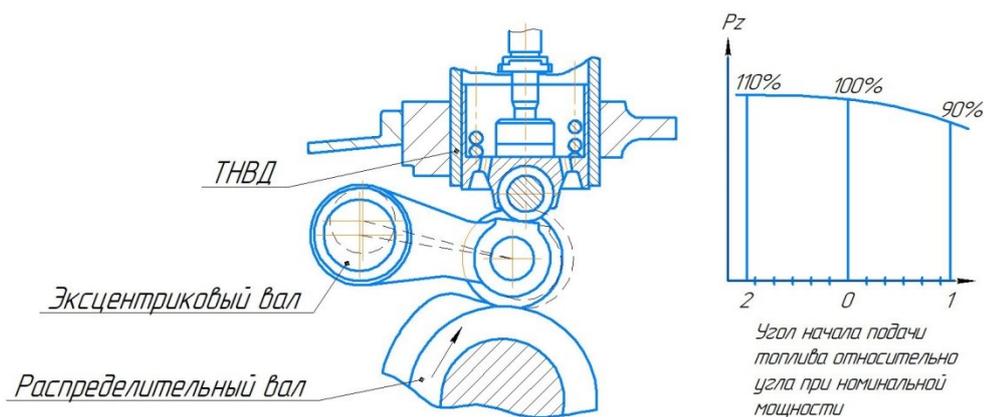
Рычажный механизм регулировки начала подачи топлива.
